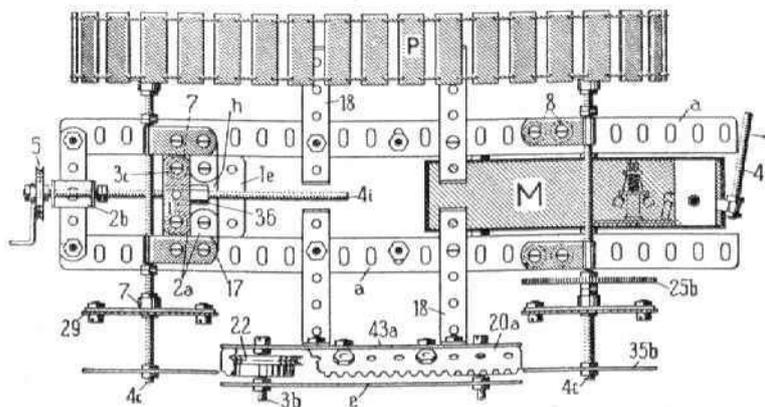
Untersicht des Raupenschleppers. An der unteren Hälfte ist das Raupenband weggelassen, um die Triebräder und Raupenhalter zu zeigen. Der Federmotor wird durch den Schalthebel Nr. 4 ein- und ausgeschaltet.
